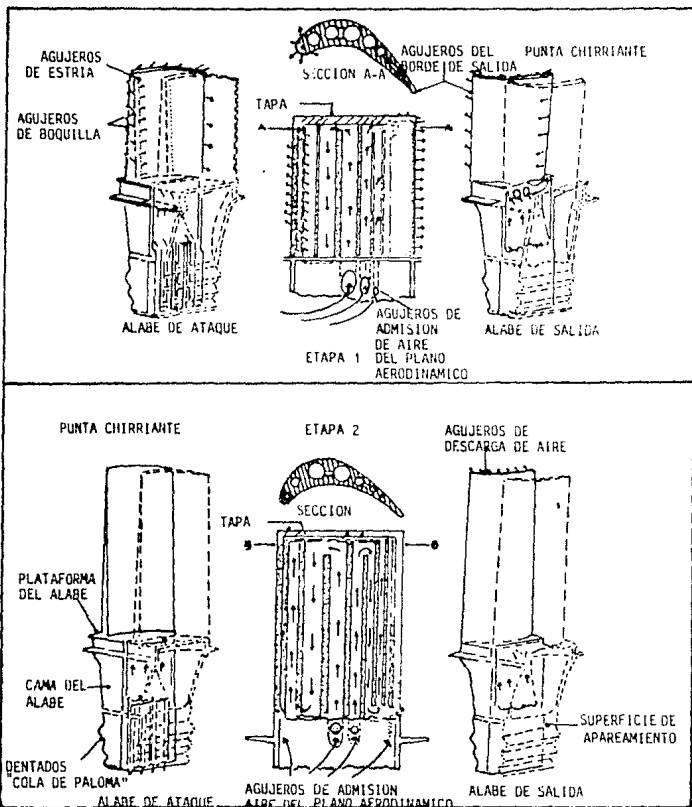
Enfriamiento de los álabes del rotor de la turbina de alta presión.
